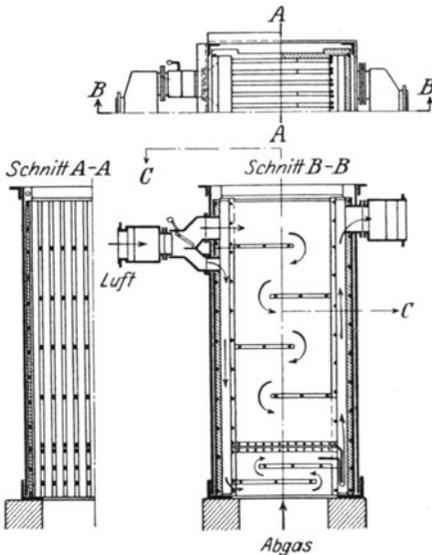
Platten-Lufterhitzer der Mantle Engineering Co., Pittsburg, Pa.
